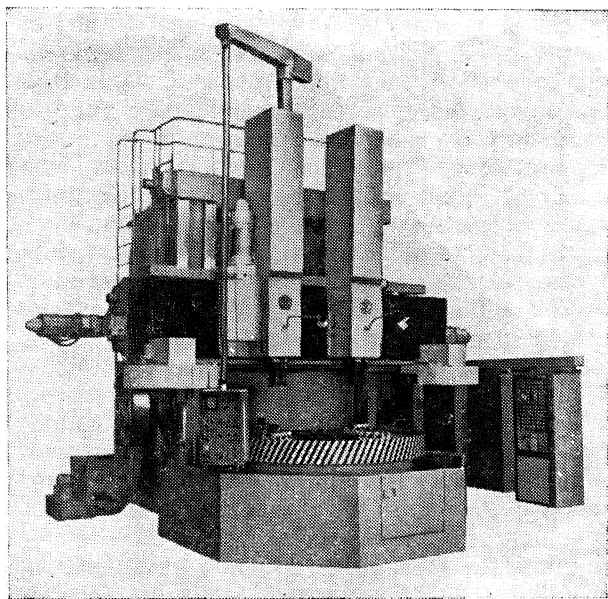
Токарно-карусельный двухстоечный универсальный станок мод. 1А525МФ3
